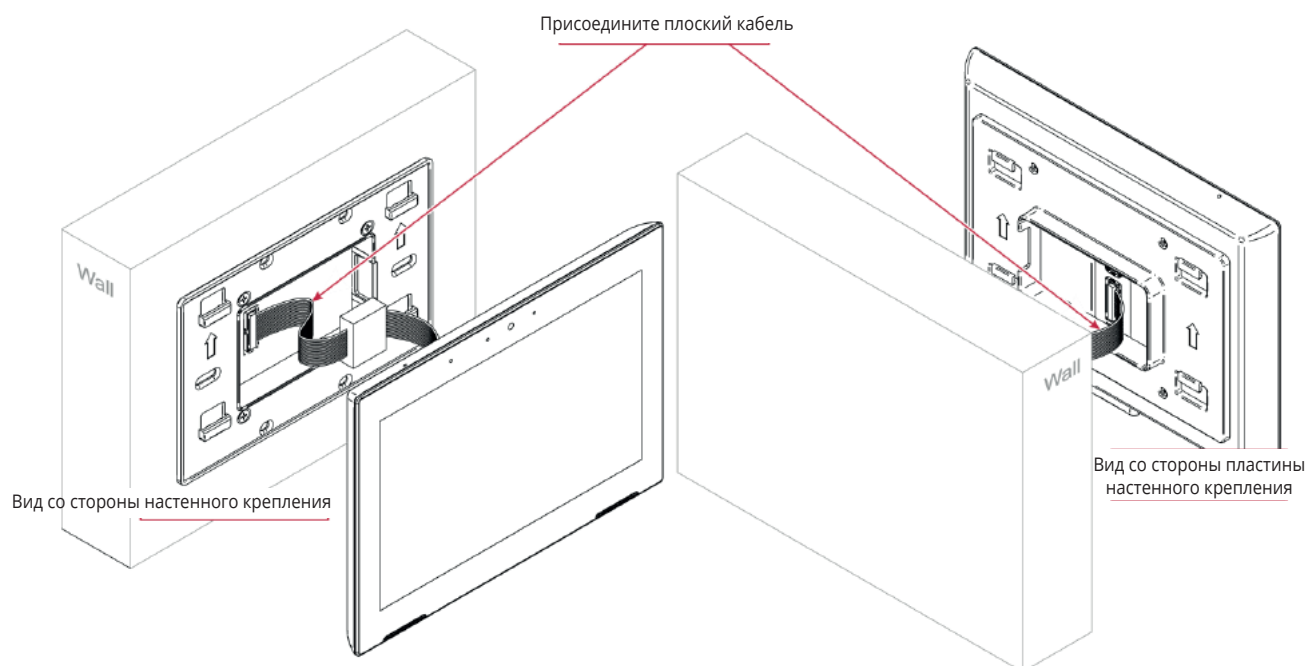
Установка соединительного плоского кабеля на настенном креплении
